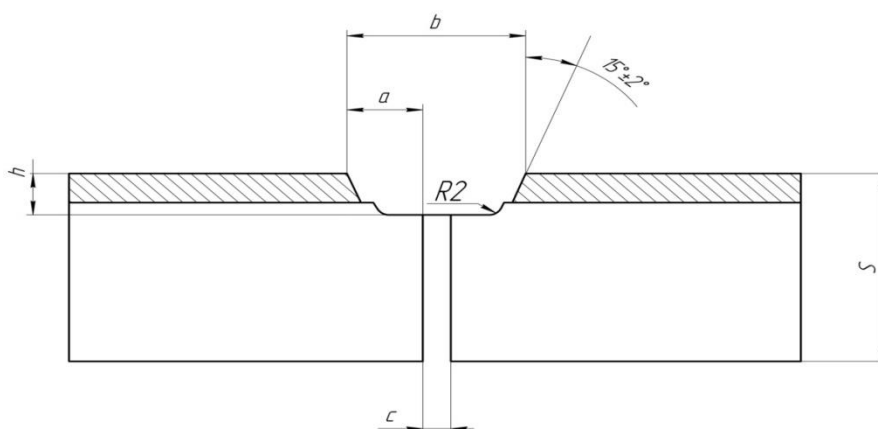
Форма разделки кромок листов двухслойных сталей при автоматической сварке
